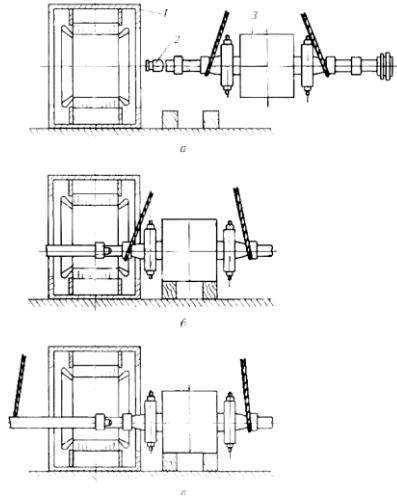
Схема ввода ротора в статор с использованием удлинителя: а - начало ввода, б — установка ротора на шпалы; в — закрепление стропа на удлинителе; 1 — статор; 2 — удлинитель вала; 3 — ротор
